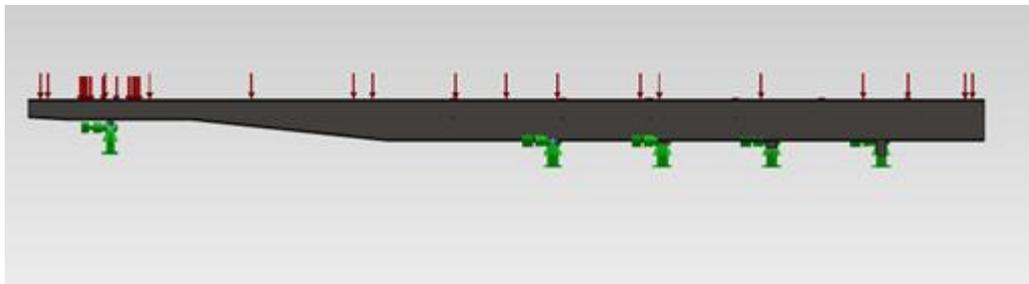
Ubicación de fuerzas y restricciones en la estructura.⁸⁹
